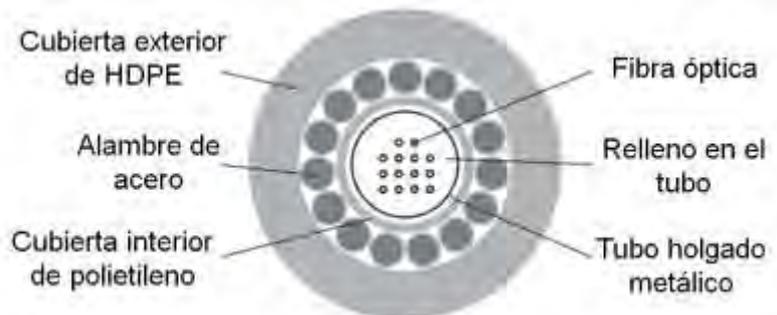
28: Estructura de cable con tubo holgado metálico [53]
